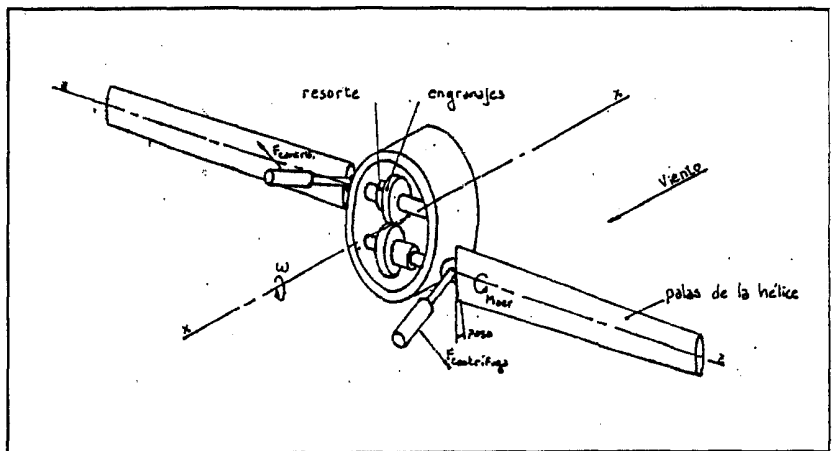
Sistema centrífugo de control diseñado por el Director de Beca
